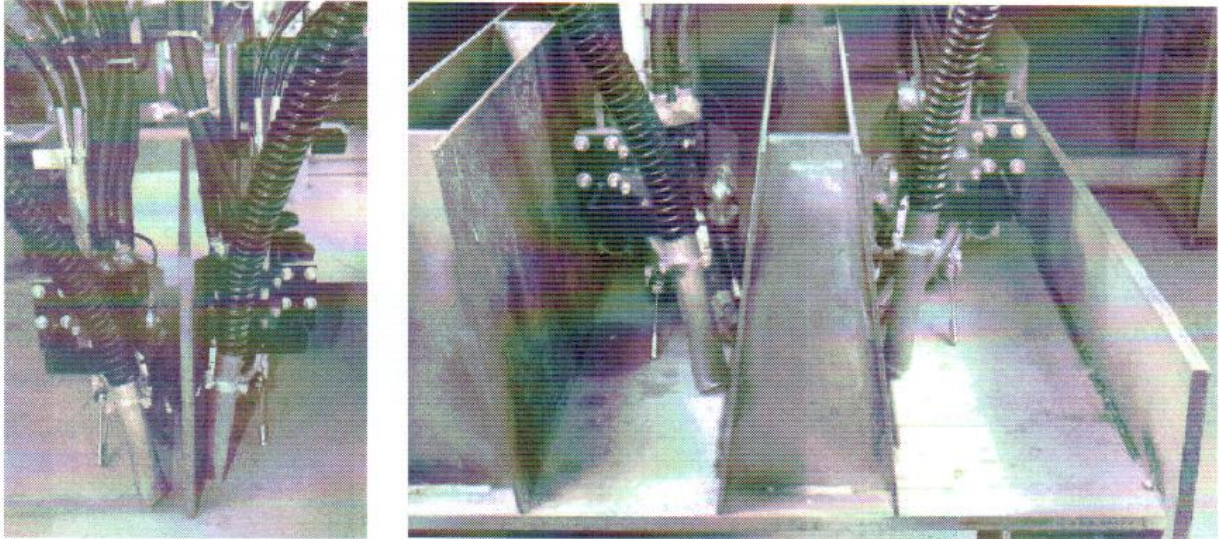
Схема зварювання на зварювальному порталі, одночасно двома зварювальними головками.
